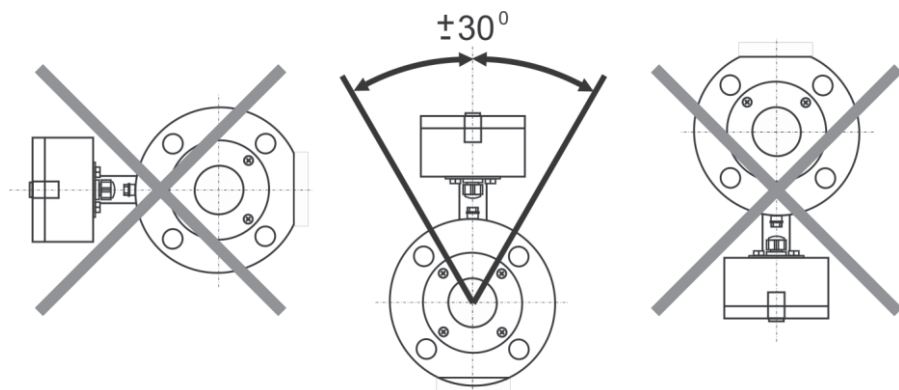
Допускаемая ориентация расходомера при установке в горизонтальные и наклонные трубопроводы
